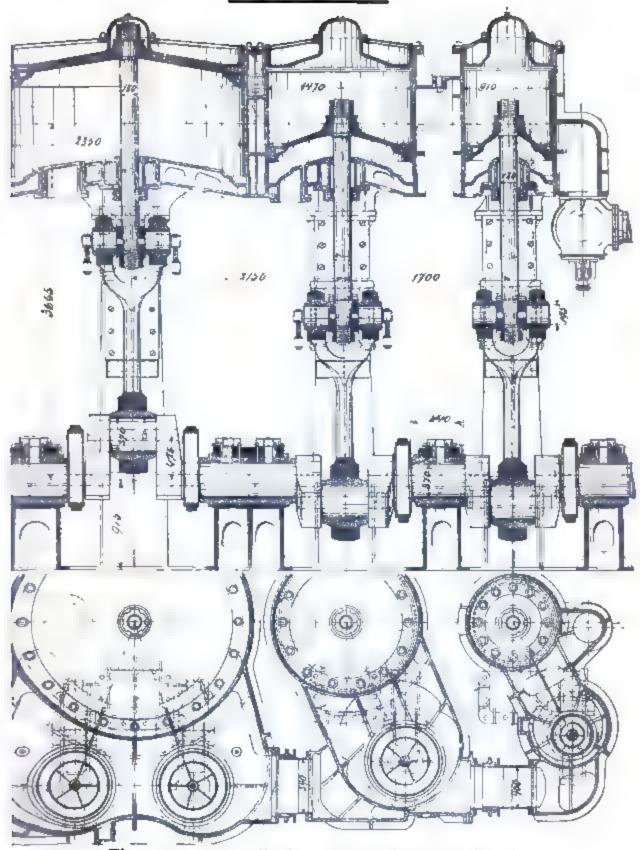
Dreifs.ch-Expansionsmaschine.*)
